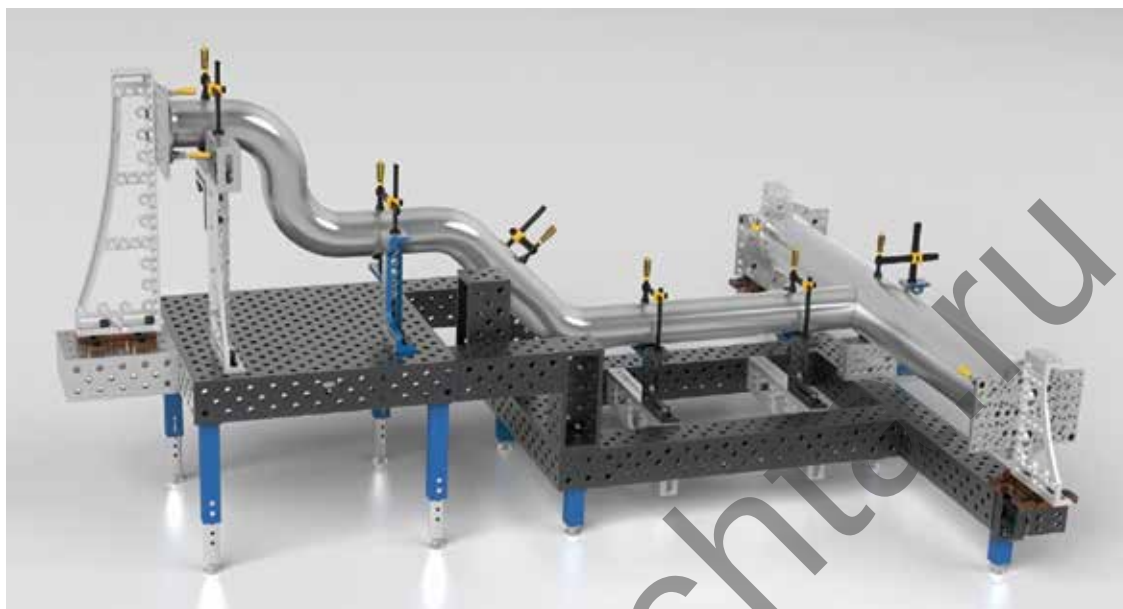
Пример приспособления для сварки труб с установленными составными частями трубы
